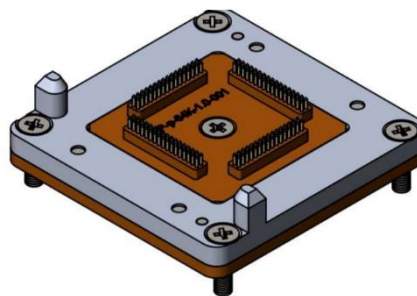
Внешний вид контактирующего устройства башни-приемника
